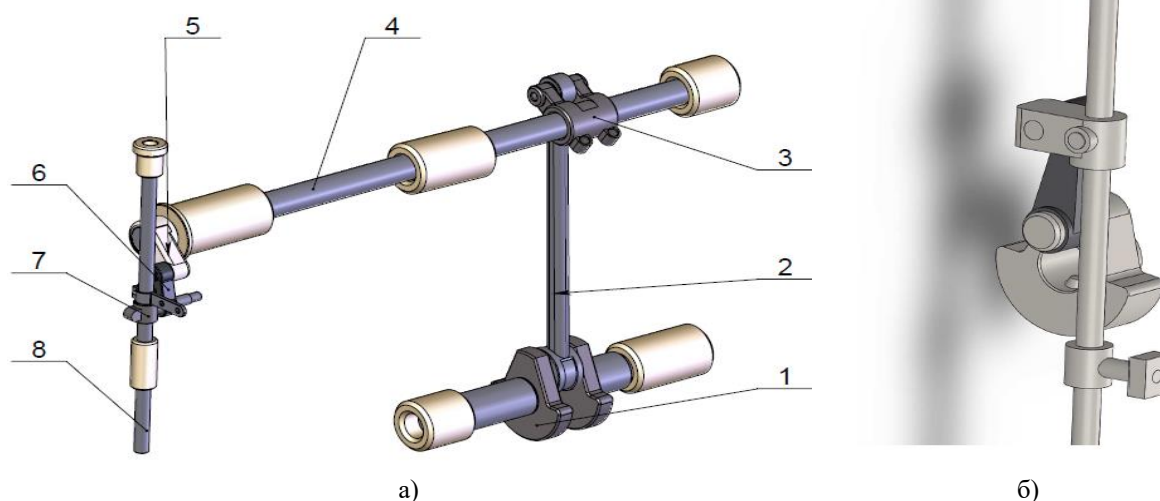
конструктивні схеми механізмів голки: а – шести ланковий (М1), б) – обернений дезаксіальний чотирьохланковий
